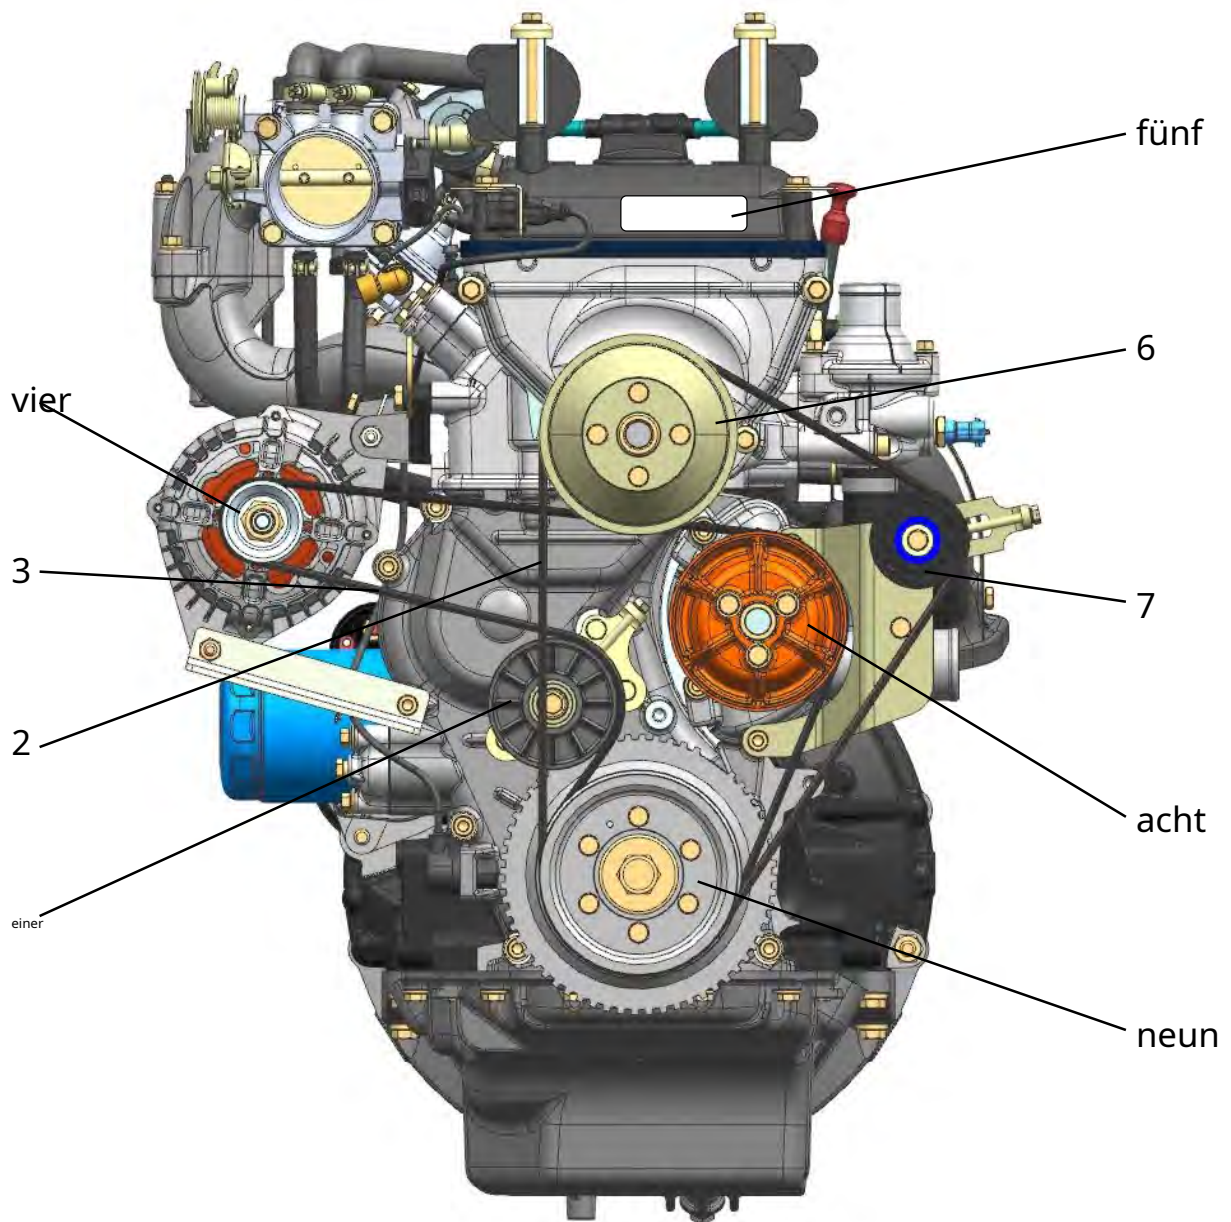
Frontansicht des Motors ohne Servopumpe:
